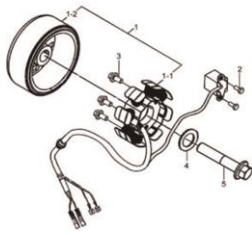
MOTOR DE PARTIDA (P05-C170-0002)
